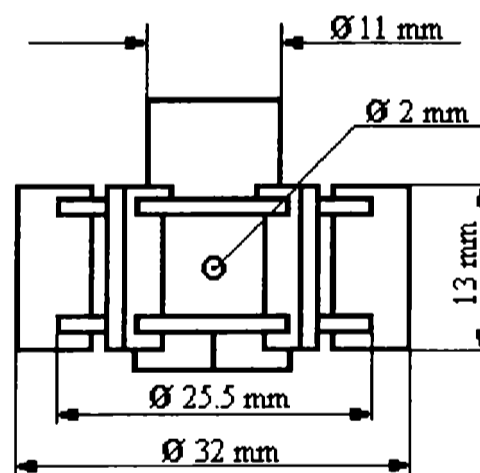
Vista frontal de la turbina de impulsión, dimensiones principales.
